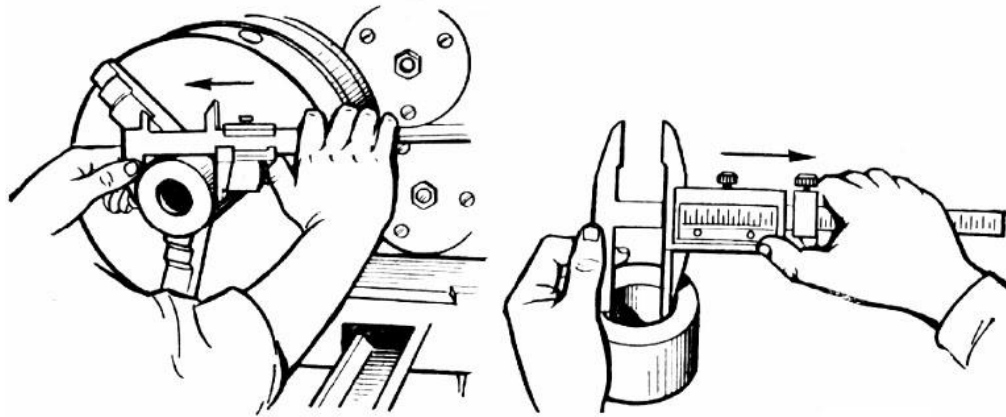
Вимірювання штангенциркулем зовнішніх (а) та внутрішніх (б) розмірів закріпленої деталі
